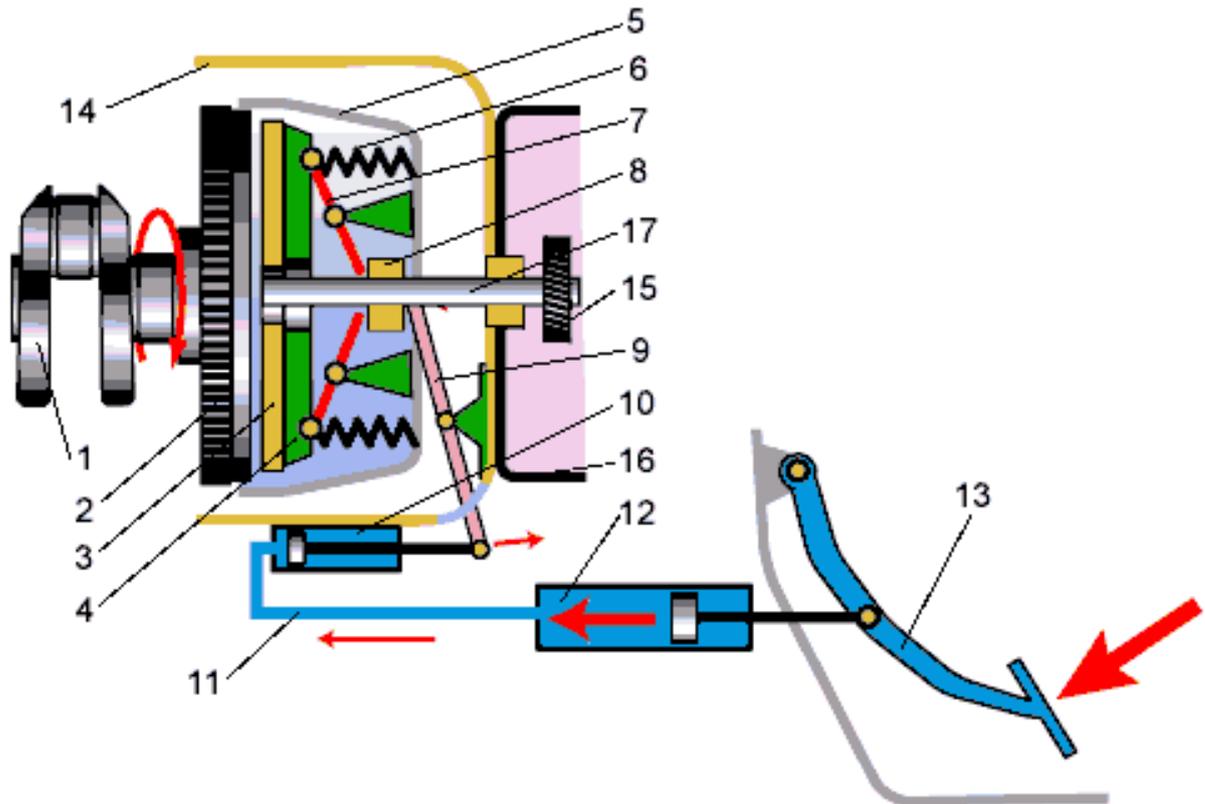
Схема гидравлического привода выключения сцепления и механизма сцепления
